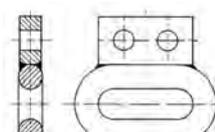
angeschweißte Mitnehmer zur Aufnahme verschiedener Vorrichtungen
